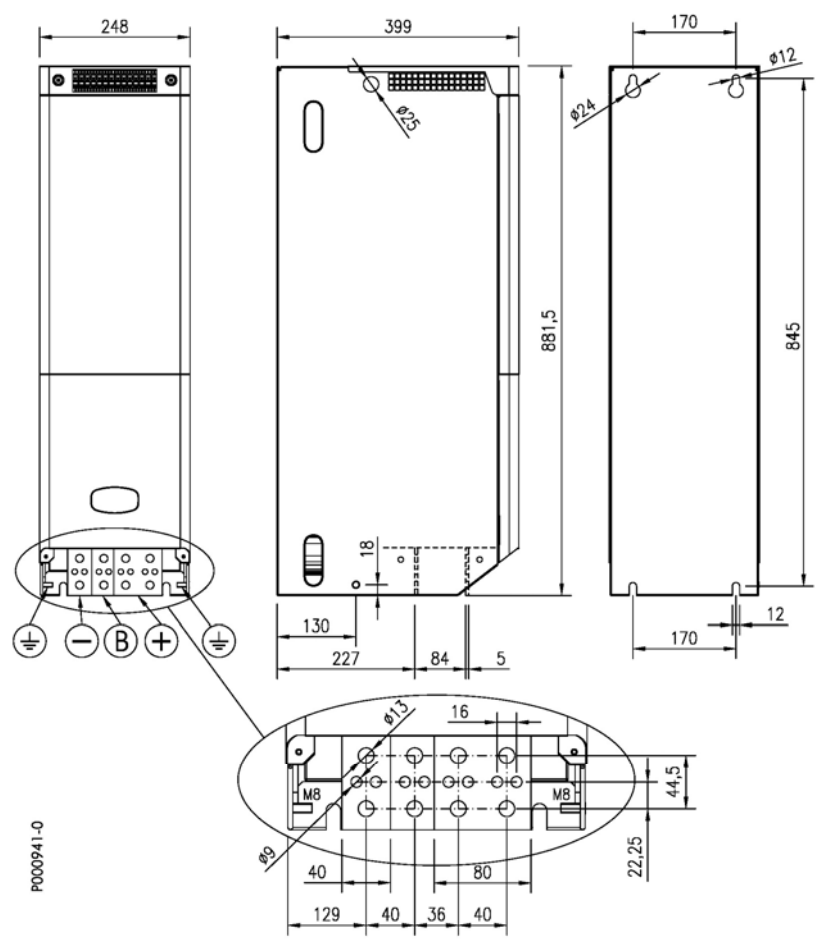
Dimensões e pontos de fixagem dos módulos de frenagem BU600/BU700
